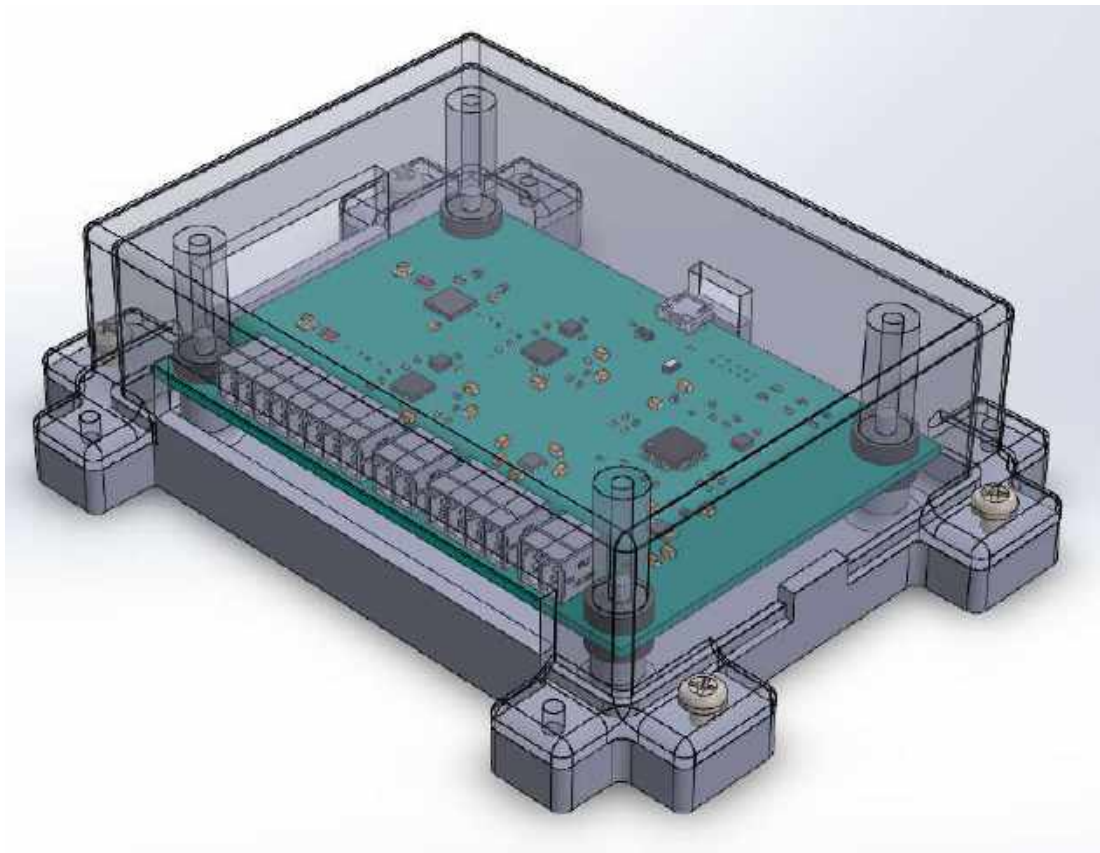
3D-модель готового корпусу з ЕМ.
